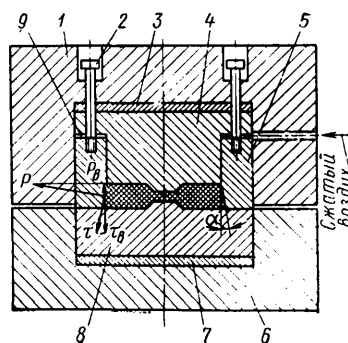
Штамп для изготовления повок методом осаждения: 1 — верхний корпус; 2 — тяги; 3 — верхняя подкладная плита; 4 — пуансон; 5 — обойма; 6 — нижний корпус; 7 — нижняя подкладная плита; 8 — матрица (нижняя вставка); 9 — кольцевая полость для подачи сжатого воздуха
